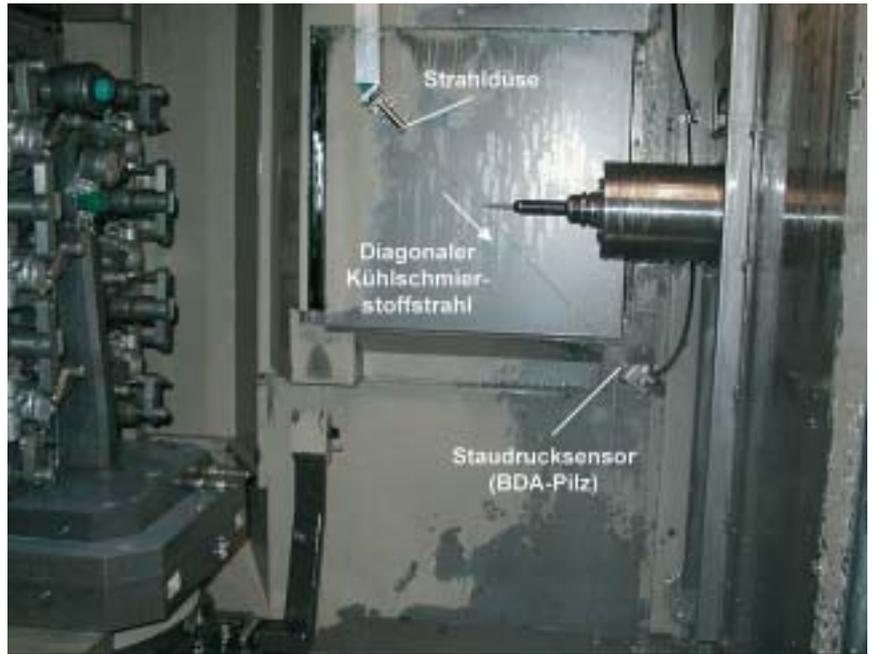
Die Staustrahlschranke kontrolliert Werkzeuge auf dem Weg zum Magazin mit einem dünnen Kühlschmierstoffstrahl
